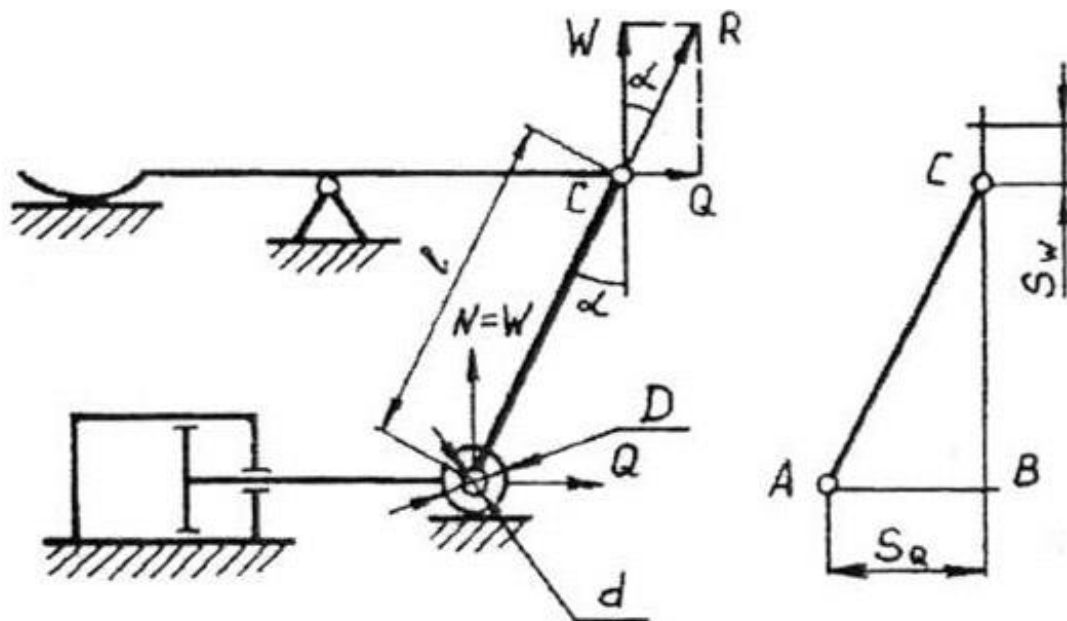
Розрахункова схема одноважільних шарнірних механізмів
